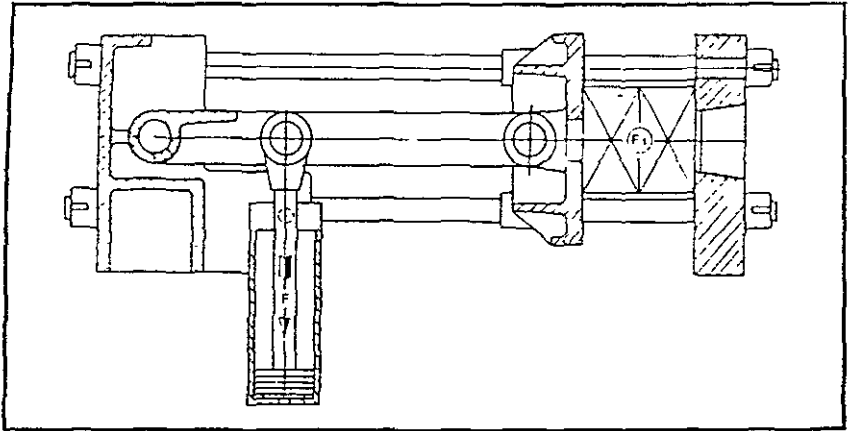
Cierre de Moldes Tipo Rodillera, Accionado por un Cilindro Hidráulico.
